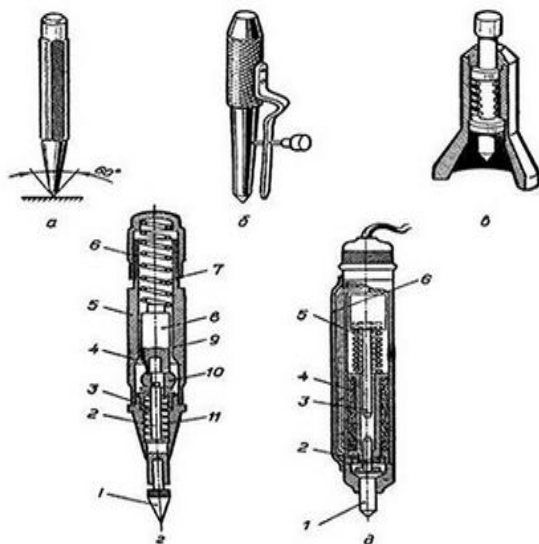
Кернери: *а* – звичайний; *б* – кернер-циркуль; *в* – кернер-колокол (центрошукач); *г* – механічний (пружинний): (1 – кернер; 2 – стержень; 3,5,6 – згвинчувані частини; 4 – плоска пружина; 7,11 – пружини; 8 – ударник; 9 – заплечики; 10 – сухар); *д* – електричний кернер (1 – кернер; 2,5 – пружини; 3 – ударник; 4 – котушки; 6 – корпус)
